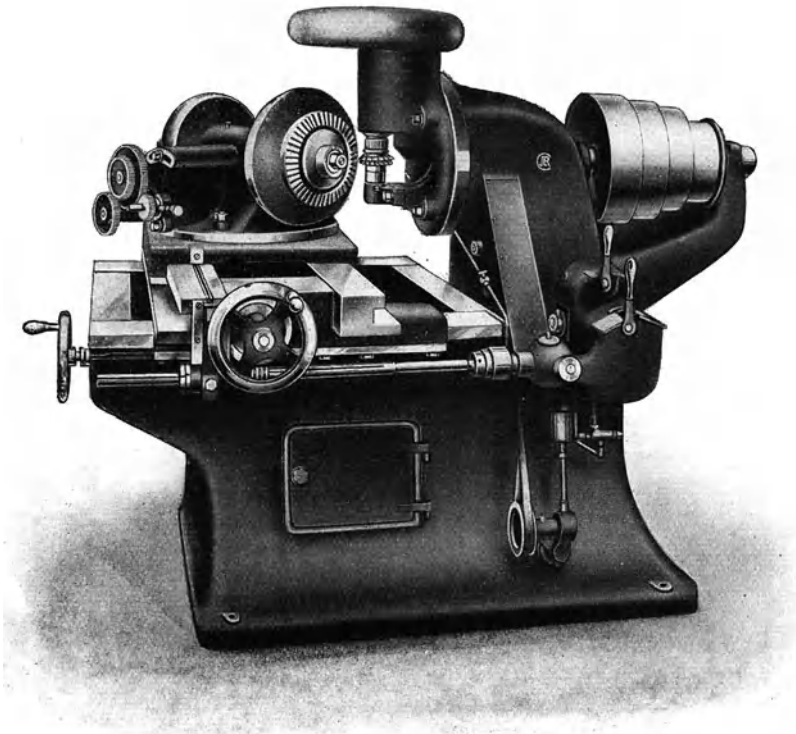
Die Kegelrädervorfräsmaschine von J. E. Reinecker.
